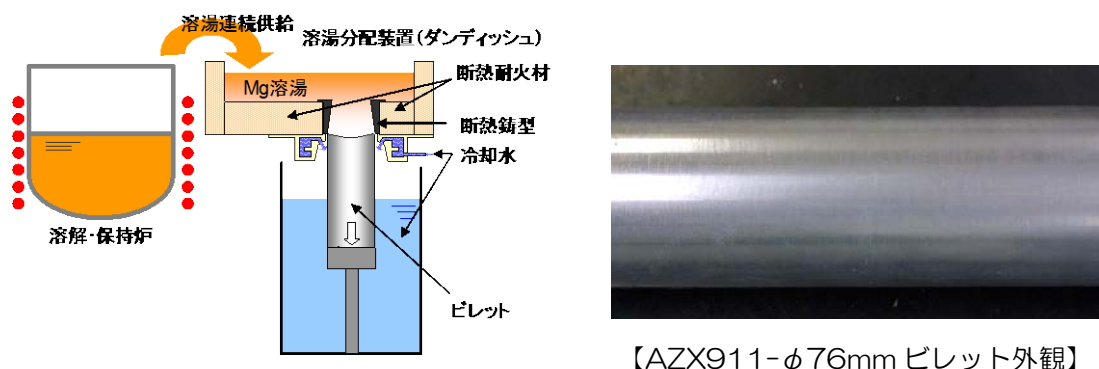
断熱鑄型による連続 casting 法と試作ピレットの外観
